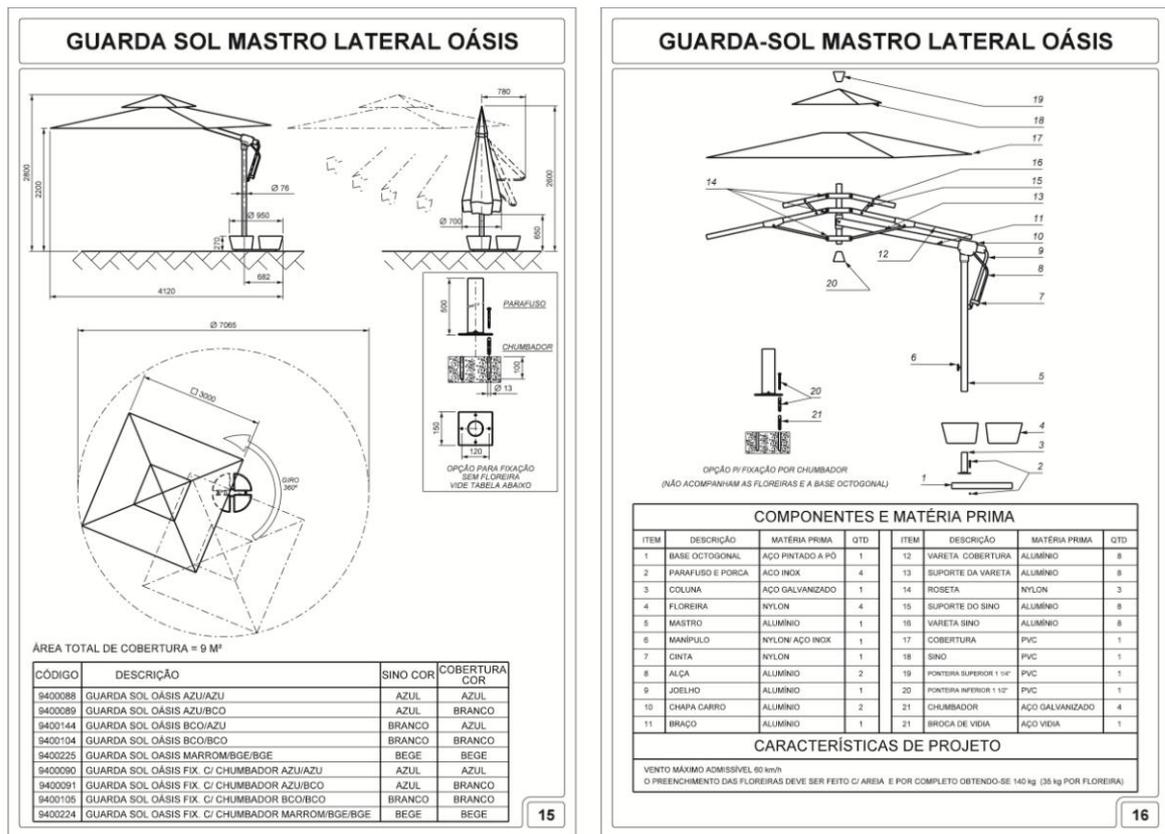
Desenho técnico do guarda sol (Fonte: <http://www.udinese.com.br/>)
